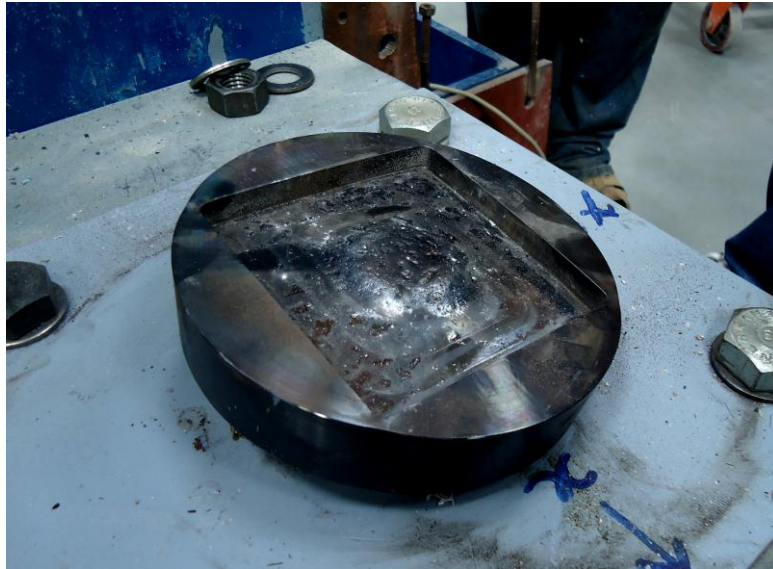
Cádhlo deformado após primeiro ensaio
